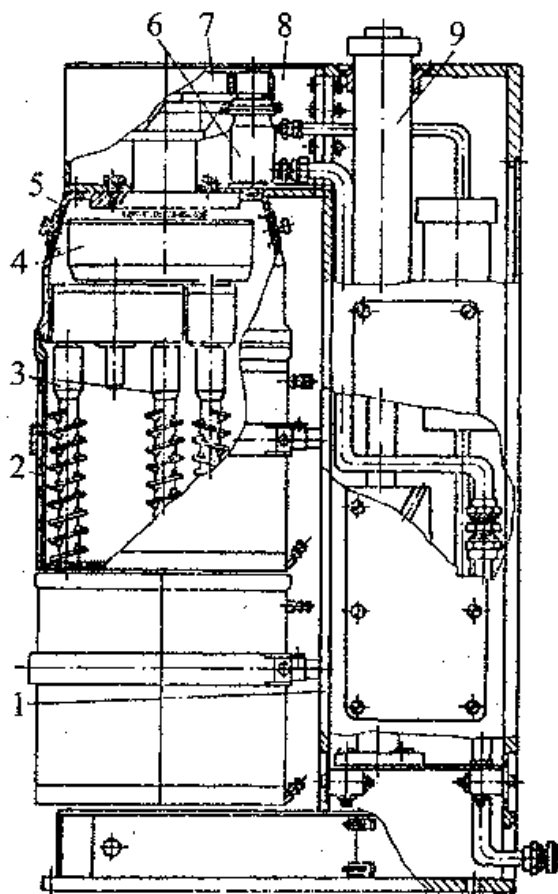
Смеситель бипланетарный шнековый [12]:
